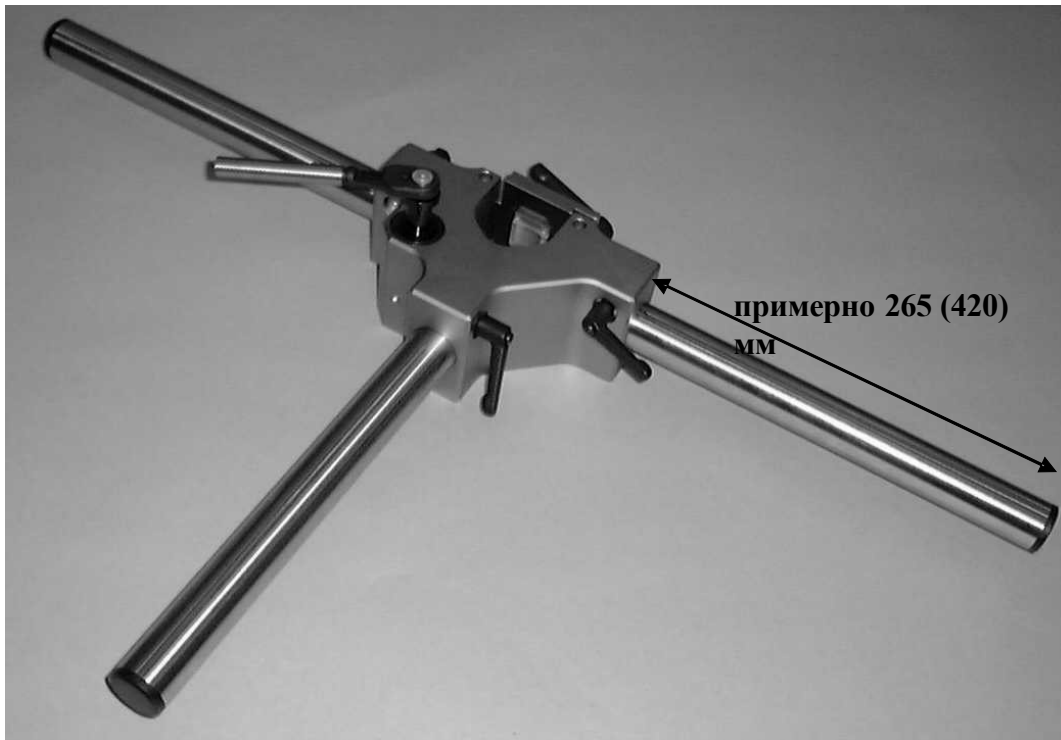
Установка опорных трубок в центральный модуль
